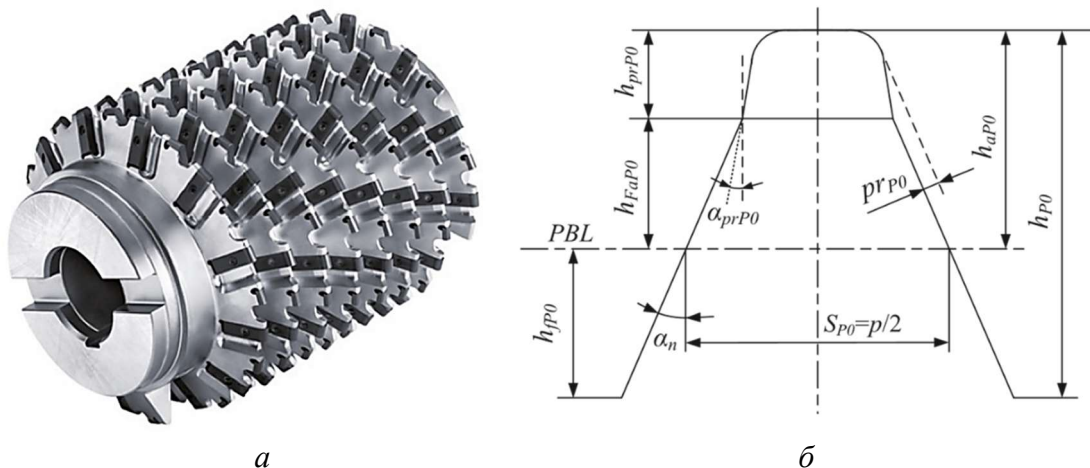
Традиційна конструкція черв'ячної фрези з протуберанцем:
